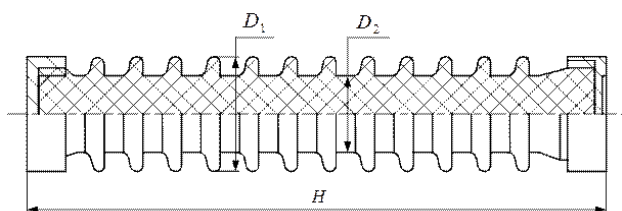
Конструкция опорного стержневого керамического изолятора ОНС
